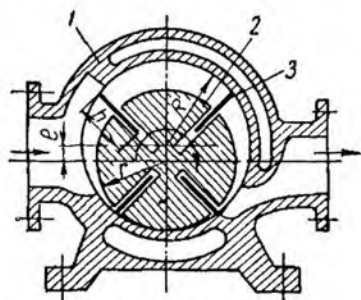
Схематичный разрез ротационного пластинчатого компрессора с вращающимся ротором:
